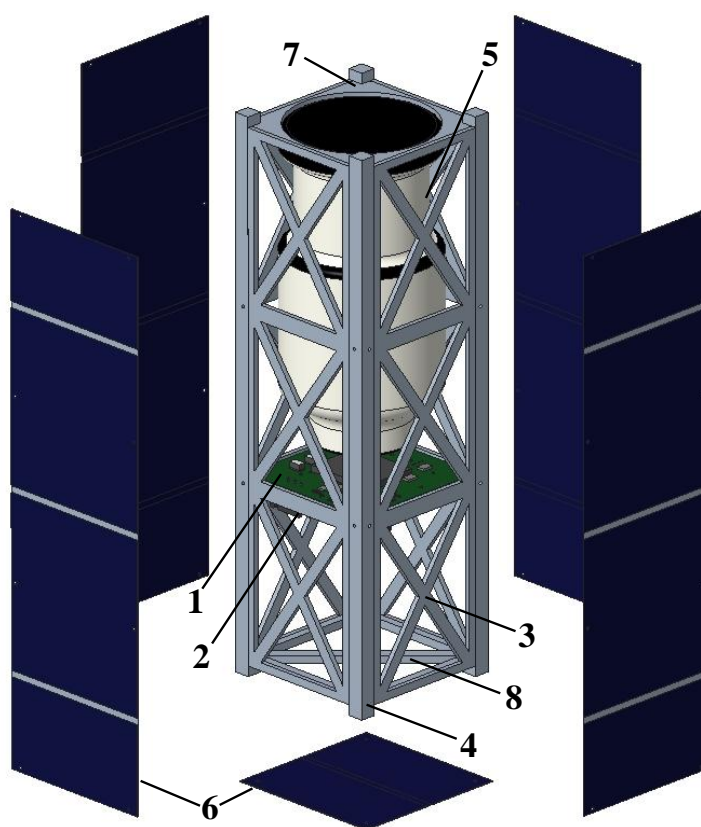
Конструкция корпуса ячейки сбора и обработки видеоинформации, где: 1 – ячейка сбора и обработки видеоинформации; 2 – рамка, на которую установлена ячейка, 3 – стенка; 4 – стойка; 5 – объектив; 6 – солнечные панели; 7 – верхняя стенка; 8 – нижняя стенка.
